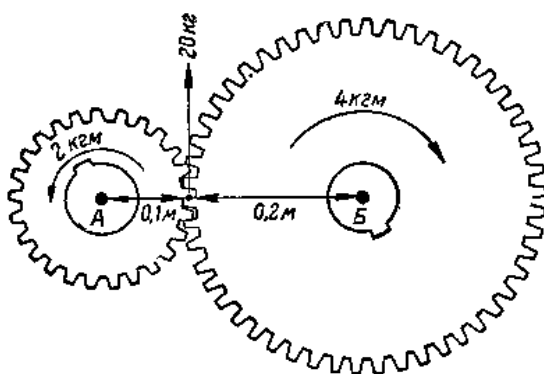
Схема передачи крутящего момента через шестерни:
